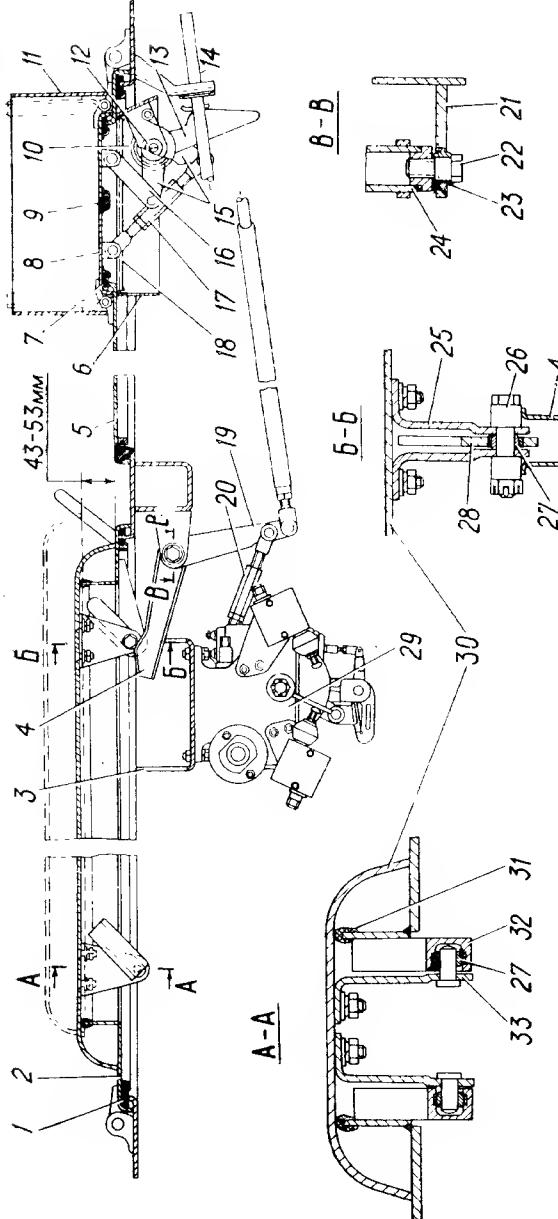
Крышки воздухопритока и воздухоотвода:
